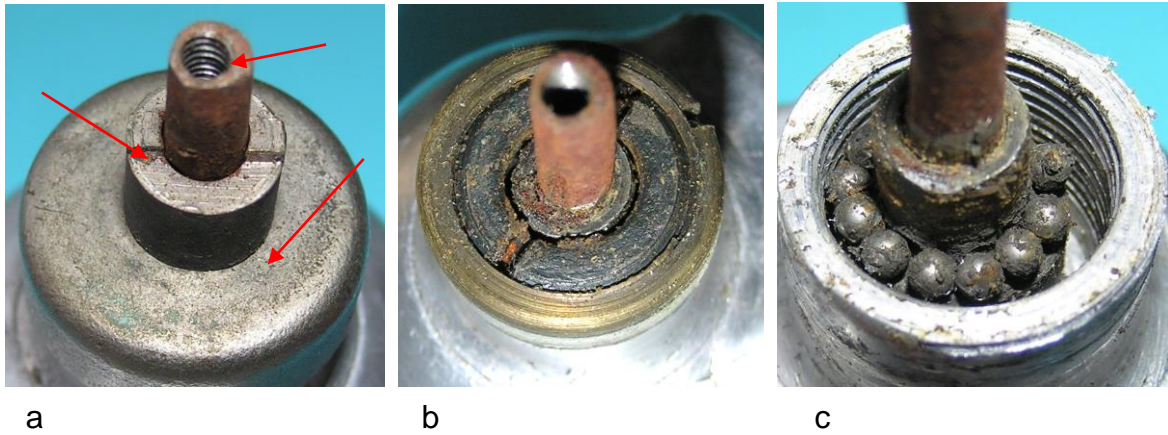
Kugellager unter dem Reibrad: a) Staubkappe und Distanzstück mit Zapfen zum Einrasten in das Reibrad, b) Eingeschraubte und gekonterte Lagerschale, c) Kugeln auf der unteren Lagerschale
